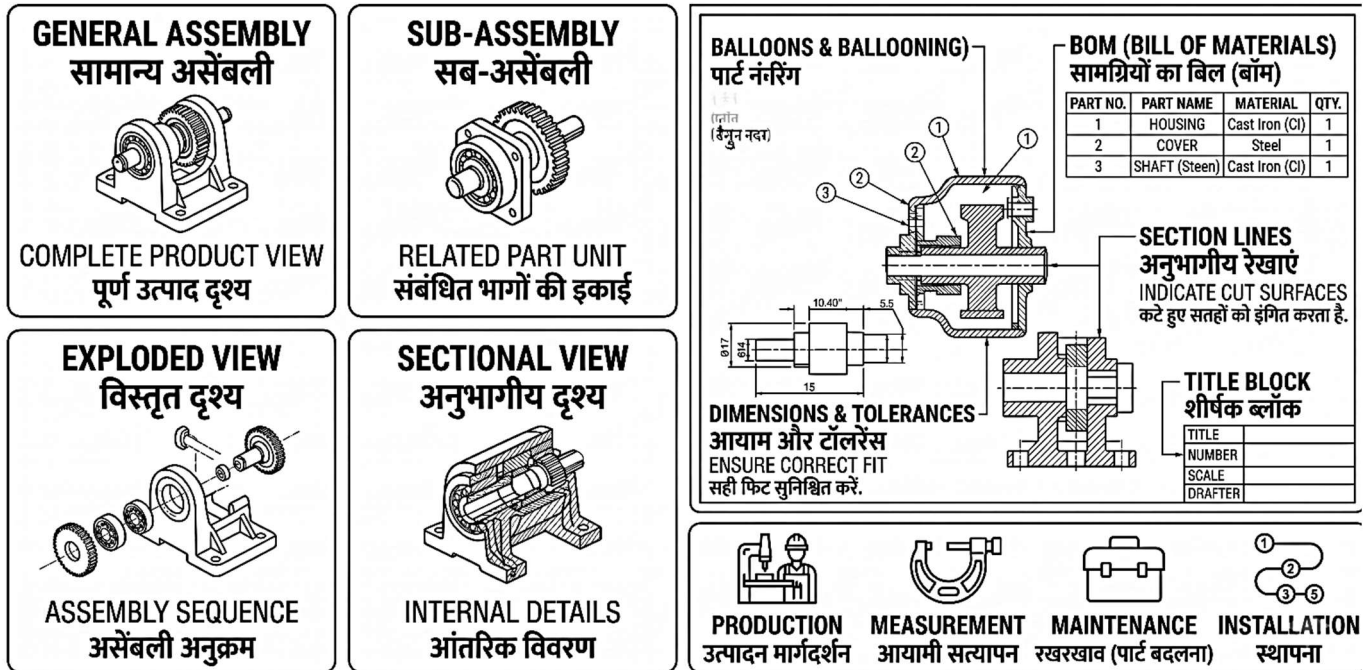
2D Assembly Drawing Fundamentals | 2D असेंबली आरेखन के मूल सिद्धांत
